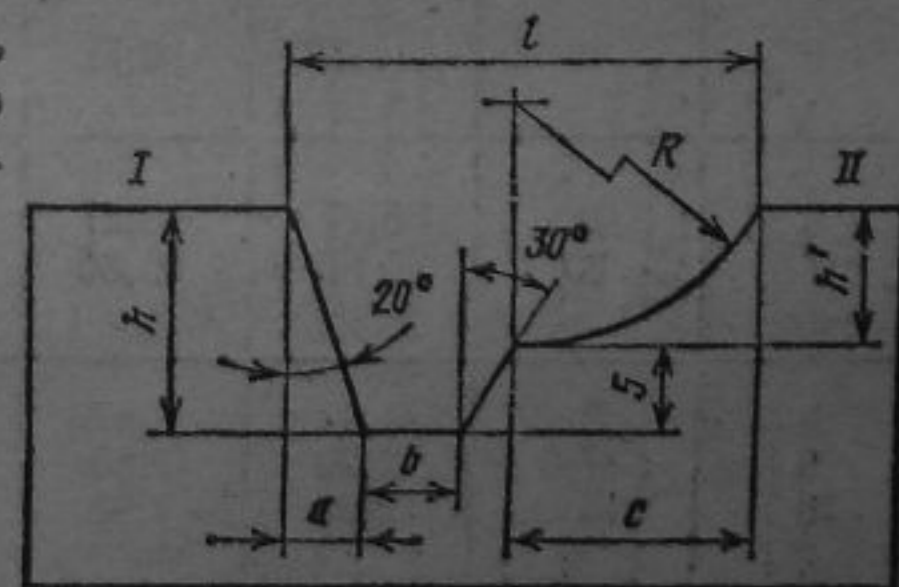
Эскиз обрабатываемой поверхности заготовки к задаче 66
